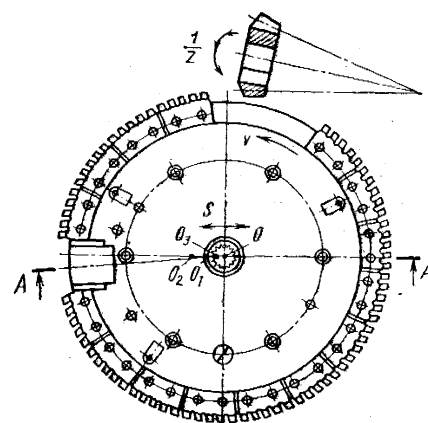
Схема нарезания конических колес круговой протяжкой
